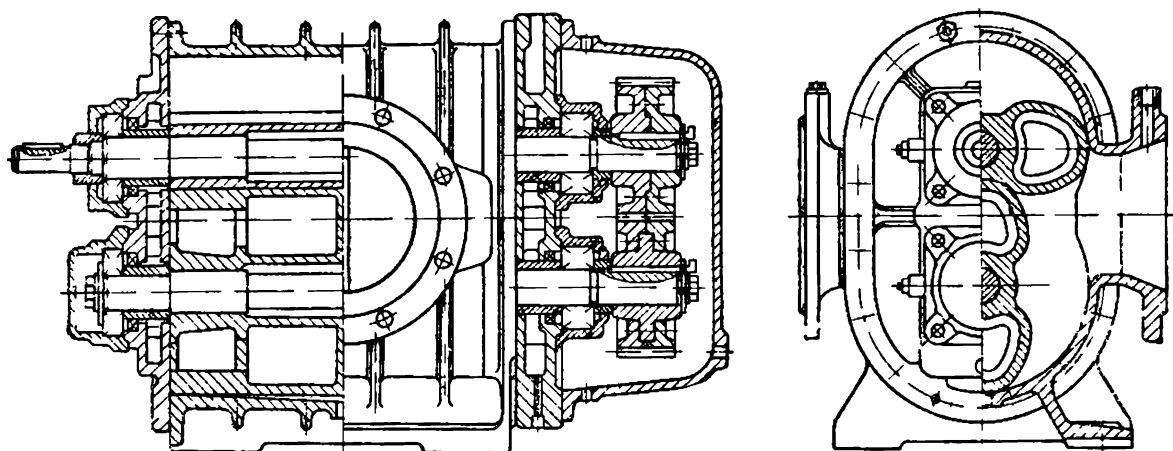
Двухроторная воздуходувка с синхронизирующими шевронными шестернями (ЕКМ, ФРГ)
